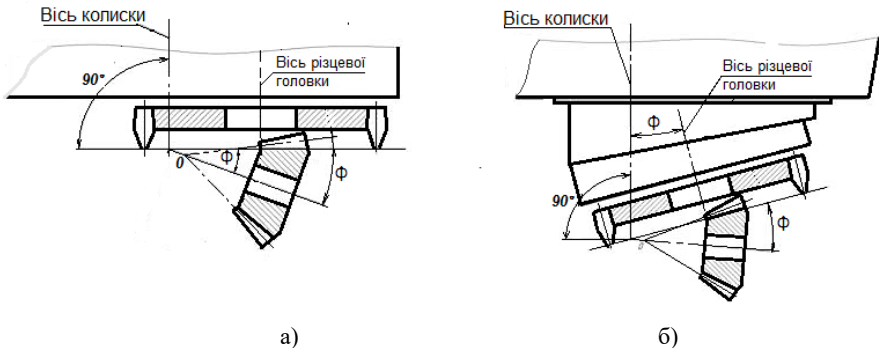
Схеми плоского і конічного твірного коліс для нарізування конічних зубчастих коліс з круговим зубом
